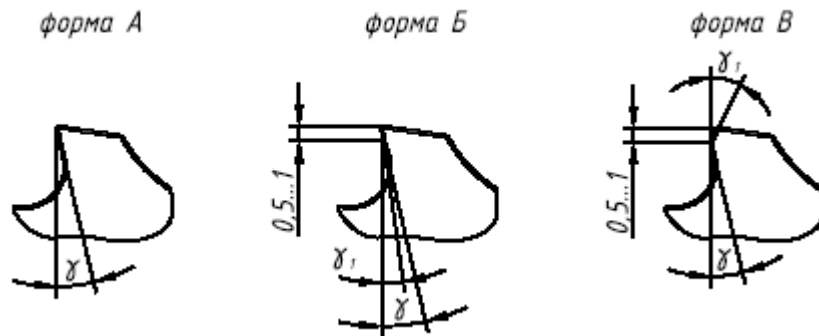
Форми загострювання передньої поверхні зубців протяжки
